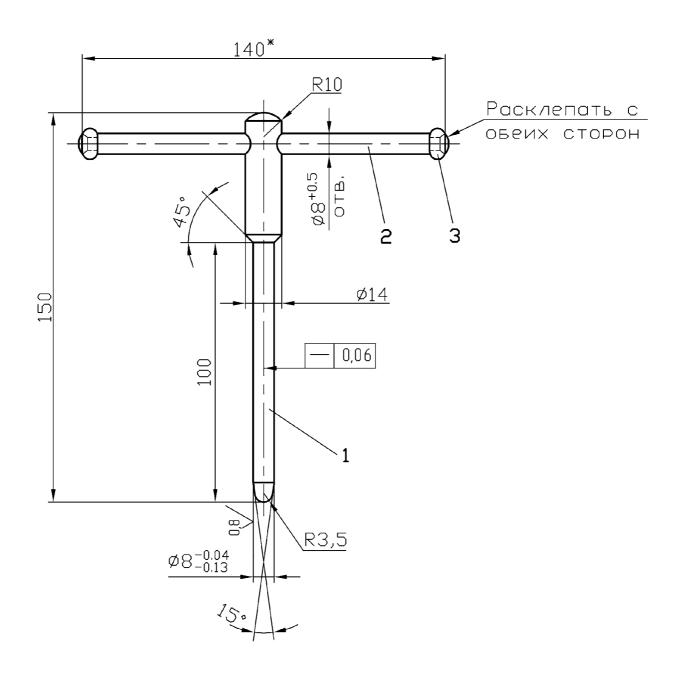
Штифт установочный коленчатого вала 3М 7820-4582: 1- корпус; 2- вороток; 3- кольцо (2 шт.)
